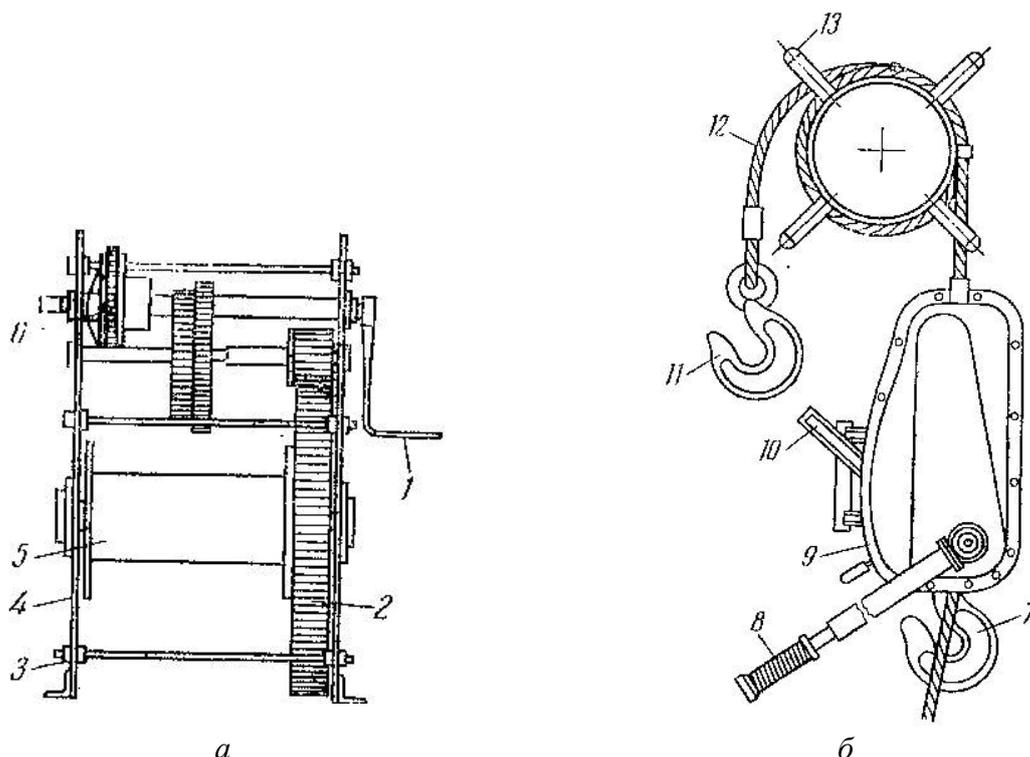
Конструкции лебедок: *а* – лебедка с ручным приводом; *б* – лебедка ручная рычажная: 1, 8, 10 – рукоятки; 2 – зубчатое колесо; 3 – стяжные болты; 4 – щеки; 5 – барабан; 6 – храповое колесо; 7, 11 – крюки; 9 – корпус; 12 – канат; 13 – катушка
